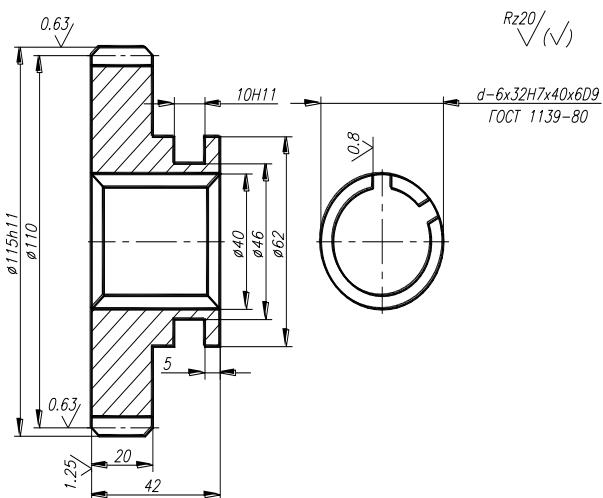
Зубчатое колесо. (Сталь 25ХГТ).
